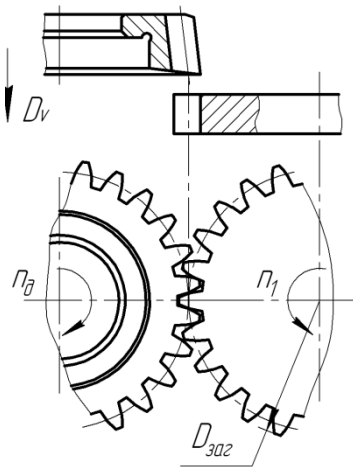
Нарізування довбачем зубів на циліндричному колесі:
